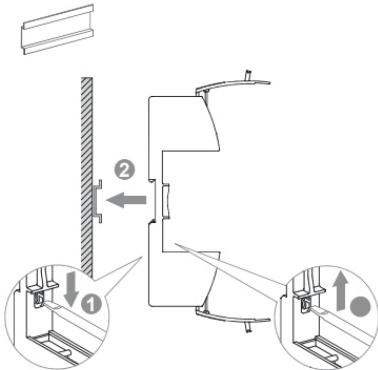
Монтаж модуля на Т-образную монтажную рейку / Figure 3 – Mounting the module on a T-shaped mounting rail
